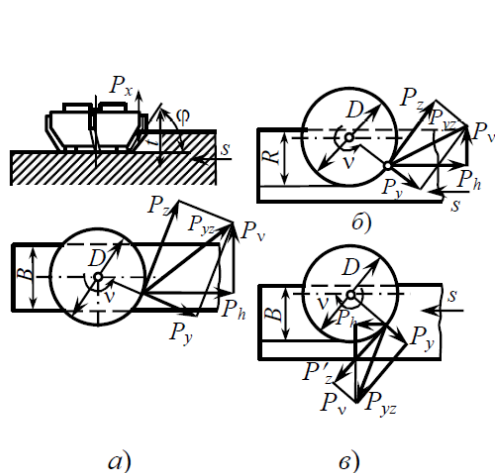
Складові сили різання при фрезеруванні циліндричною резою:
